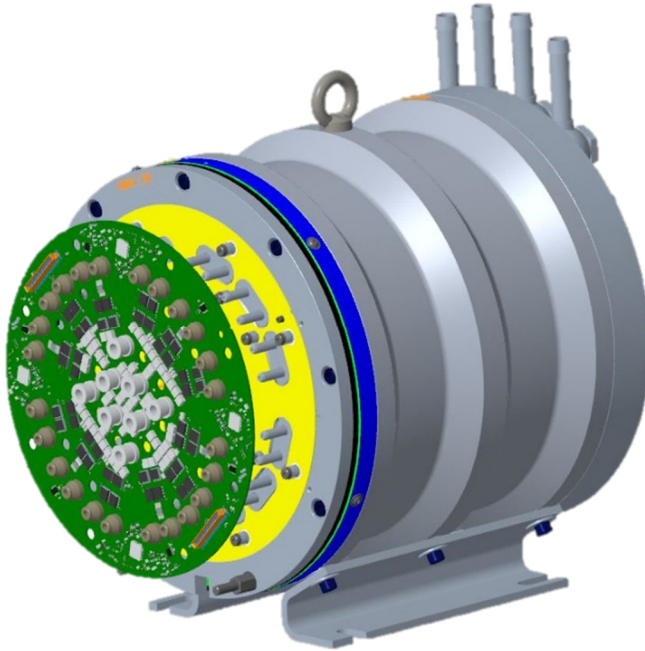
InED, Motor mit Wechselrichter in Explosionsdarstellung.
